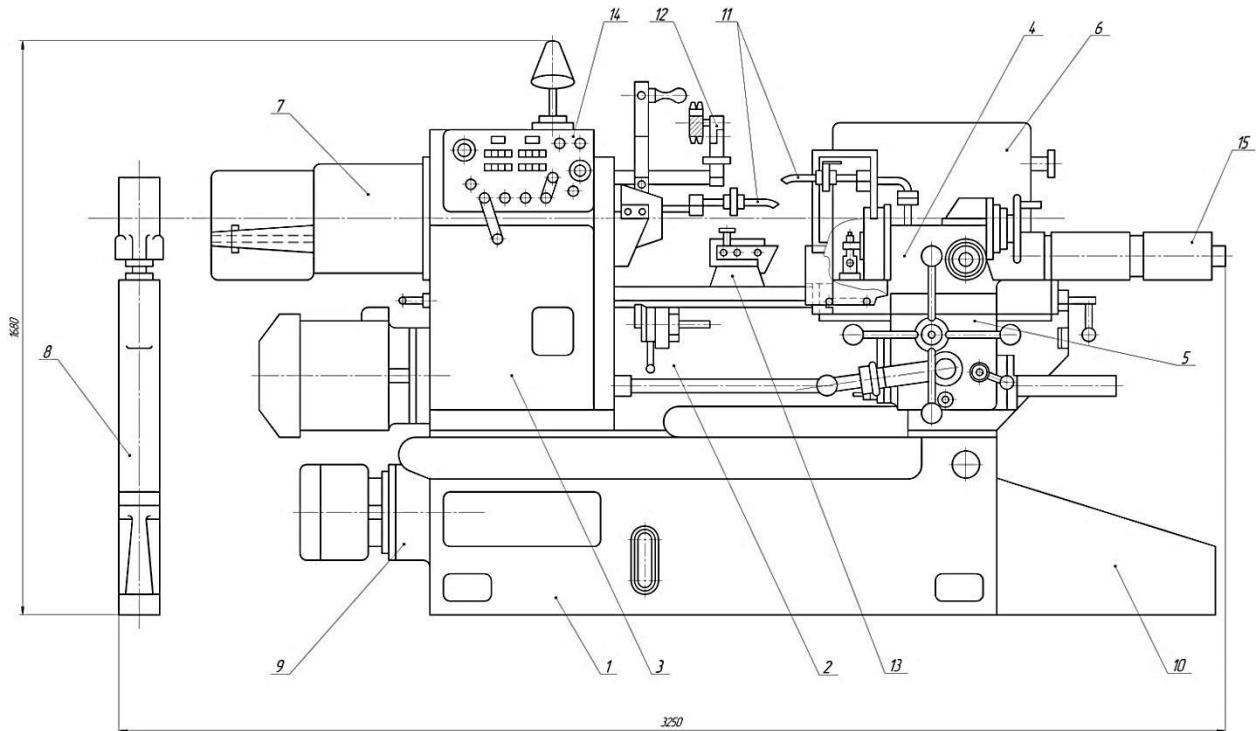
Загальний вид базової моделі верстата 1П365
